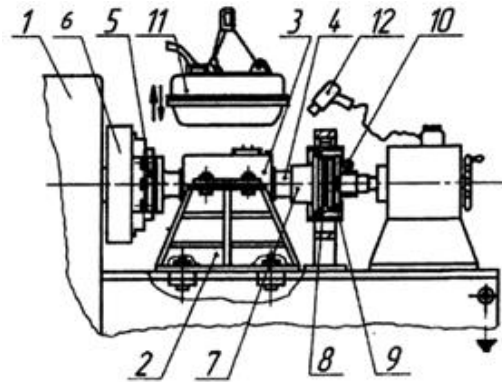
Загальний вид стенда для випробувань упорних підшипників
